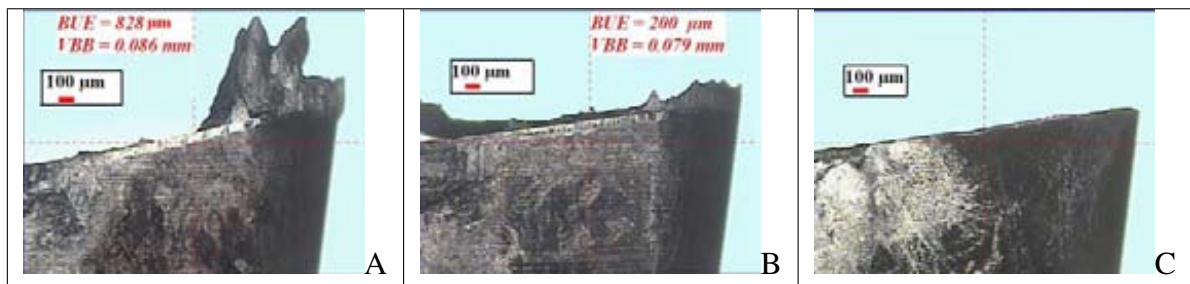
Faces de dépouille des plaquettes usées après 3000 cm<sup>3</sup> de matière usinée à sec, A. Plaquette O1, B. Plaquette S2, C. Plaquette S3.
